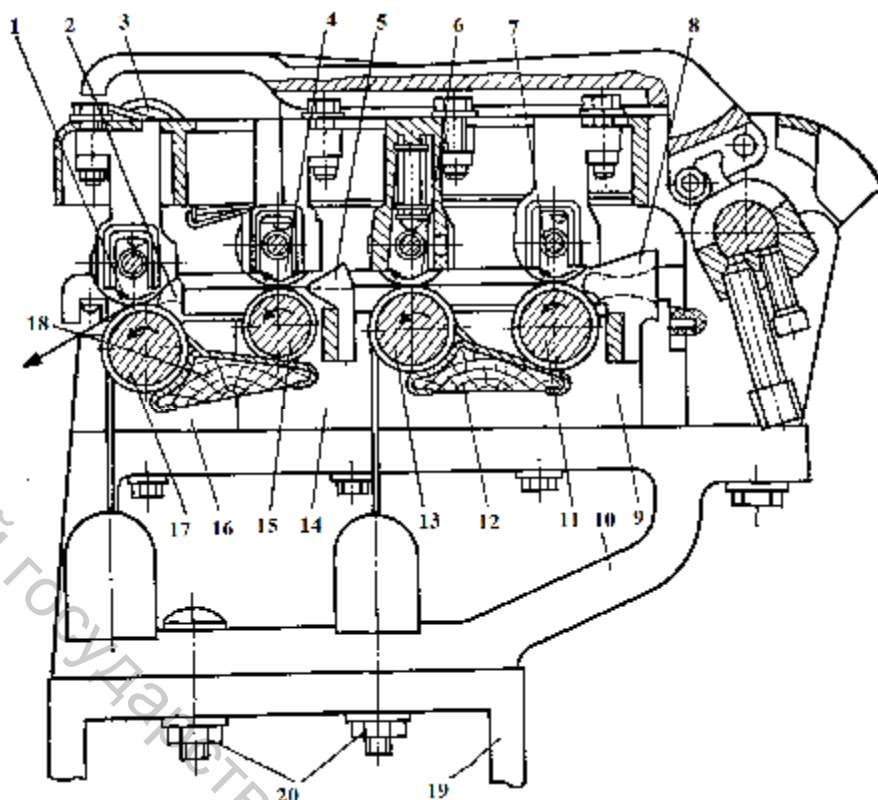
Четырехцилиндровый двухзонный вытяжной прибор с уплотнителями ленты и мычки
